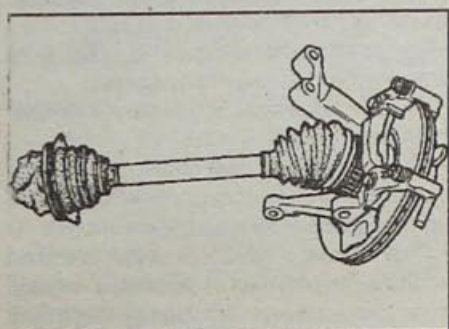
Снятие с автомобиля узла приводной вал – поворотный кулак – тормозной диск
